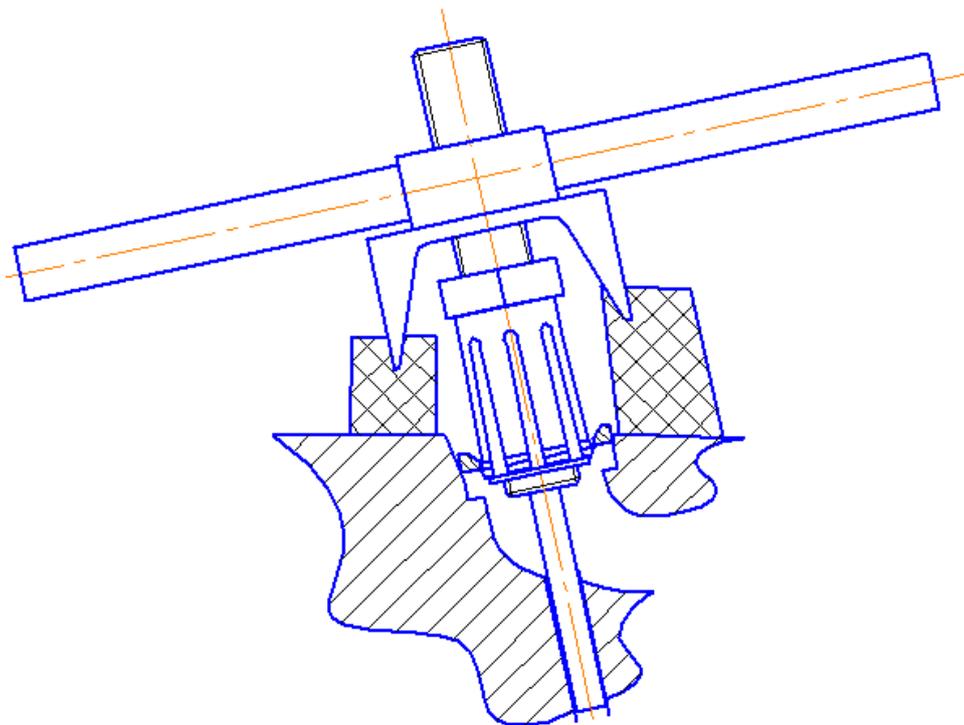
Выпрессовка кольца клапанного седла
